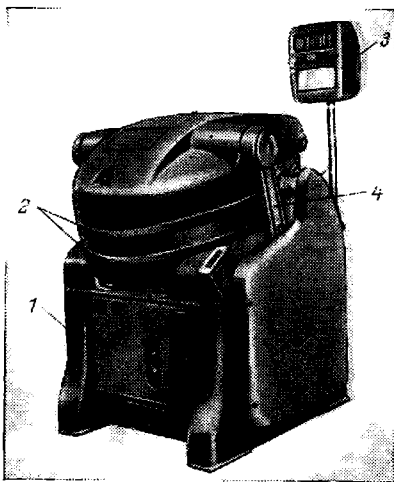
Общий вид механического двухэтажного пресса для вулканизации велопокрышек: 1 — рама пресса; 2 — пресс-формы; 3 — регистрирующий термометр; 4 — кривошипный механизм.
